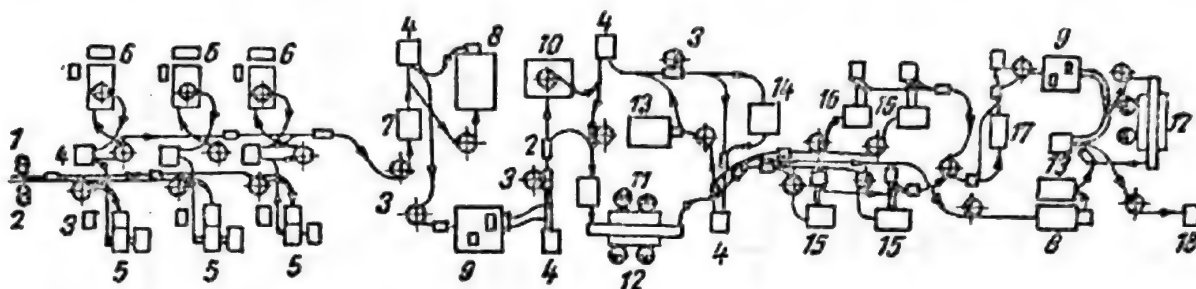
Linie semiautomată pentru montajul rulmenților radiali cu bile 6208: 1 — opritor; 2 — macaz; 3 — stocator; 4 — elevator; 5 — mașină automată de montaj selectiv; 6 — mașină automată de montaj colivii; 7 — demagnetizor; 8 — mașină automată de spălat; 9 — mașină automată de control zgomet; 10 — mașină automată de marcat electrochimic; 11 — mașină automată de control joc radial; 12 — conveier de control; 13 — mașină automată de uscat în freon; 14 — mașină automată de introdus vaselină; 15 — mașină automată de montat capace; 16 — mașină automată de montat garnituri; 17 — mașină automată de uniformizat vaselină; 18 — mașină automată de conservat.
